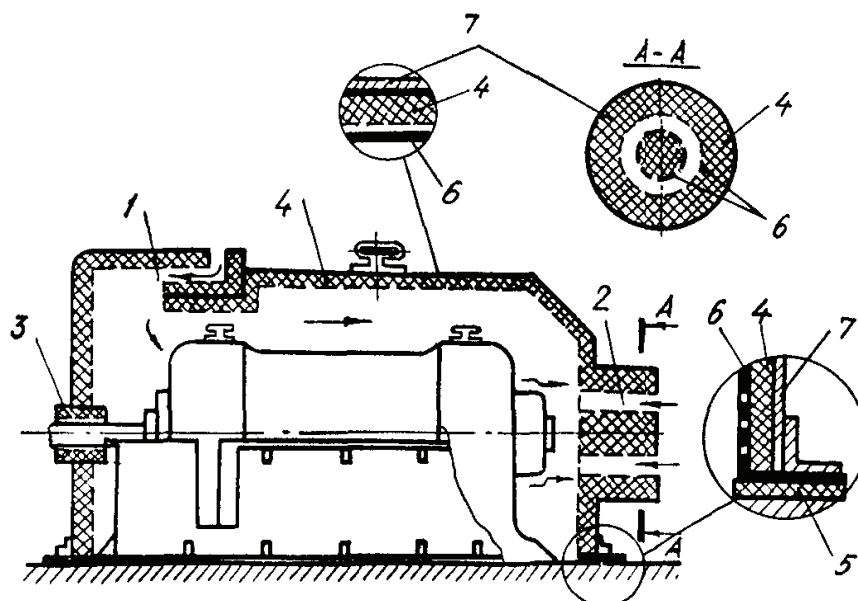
Схема звукоизолирующего кожуха: 1, 2 – глушители в отверстиях для циркуляции воздуха; 3 – глушитель в отверстии вала; 4 – звукоизолирующая облицовка; 5 – резиновая прокладка; 6 – перфорированный лист; 7 – металлический лист
